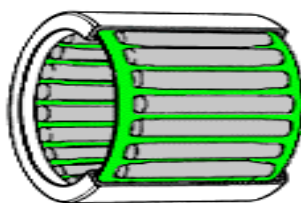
ตลับลูกปืนเม็ดกลมทรงกระบอก (Cylindrical roller thrust bearings)
